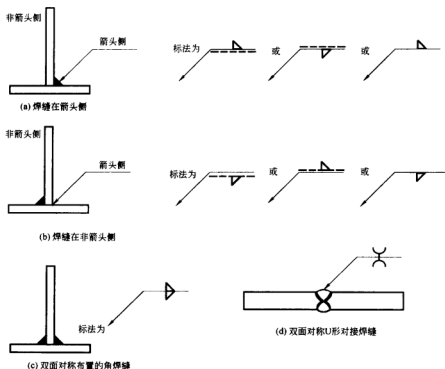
焊缝基本符号与基准线的相对位置
